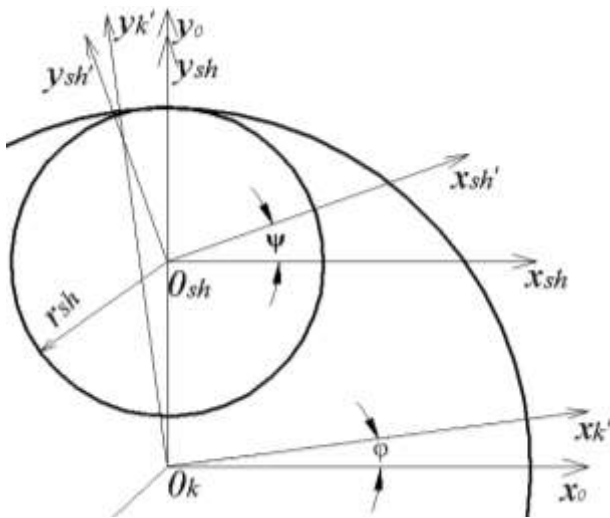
Схема преобразования систем координат колеса и шестерни в процессе обкатки
